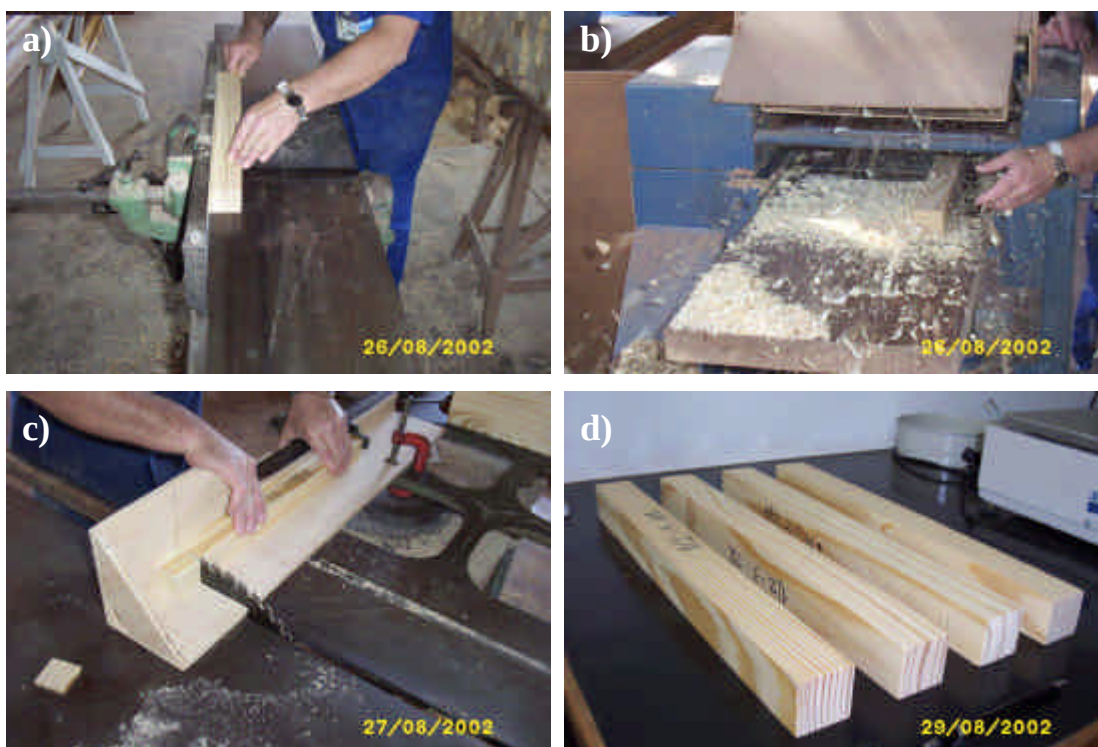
Confecção dos corpos-de-prova longitudinais. a) acerto das faces na desempenadeira; b) passagem do corpo-de-prova pela desengrossadeira; c) acerto final na dimensão desejada e d) exemplares de madeira juvenil (ao centro) e madeira adulta (nas laterais).
